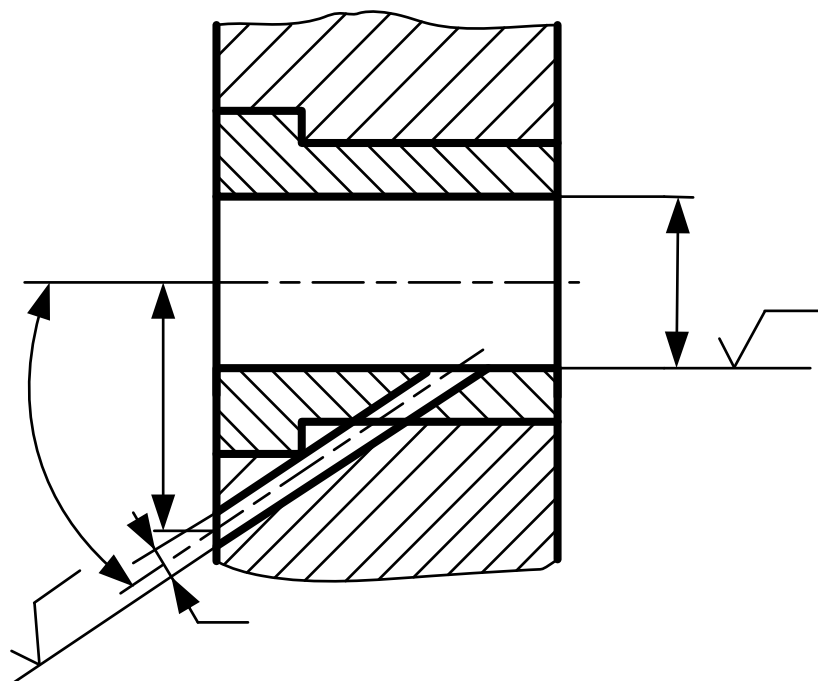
Обозначение предельных отклонений и шероховатости поверхностей на сборочном чертеже
